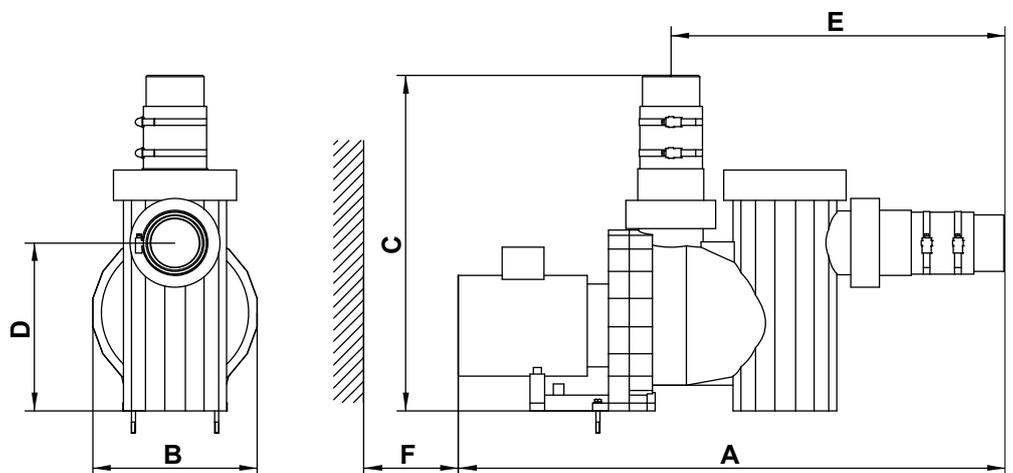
Maßzeichnung Umwälzpumpen Resort
